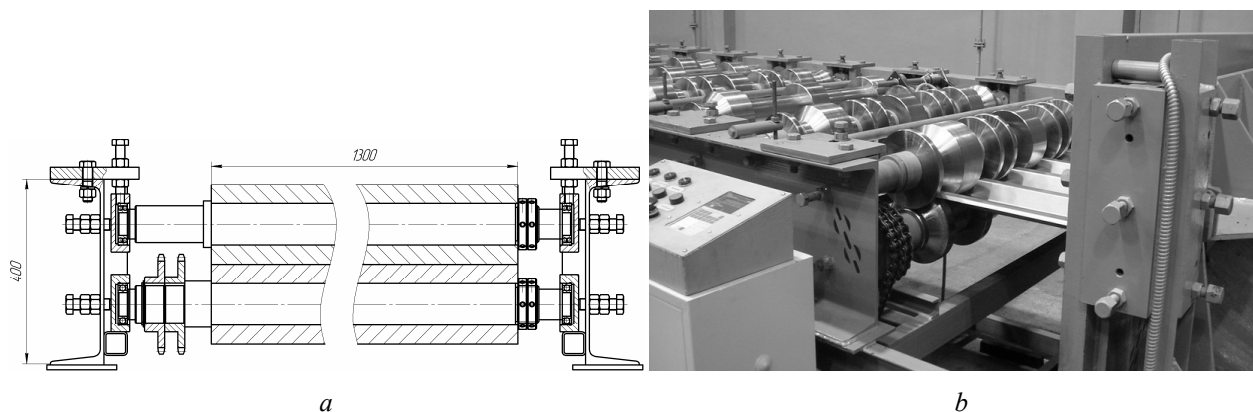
Профилегибочный стан Н44 и рабочая клеть со станиной, изготовленной из швеллеров: а – проект; б – изготовленный стан
